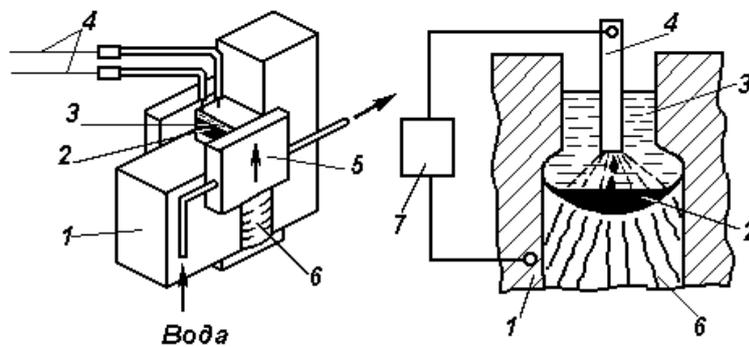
Схема процесса электрошлаковой сварки
